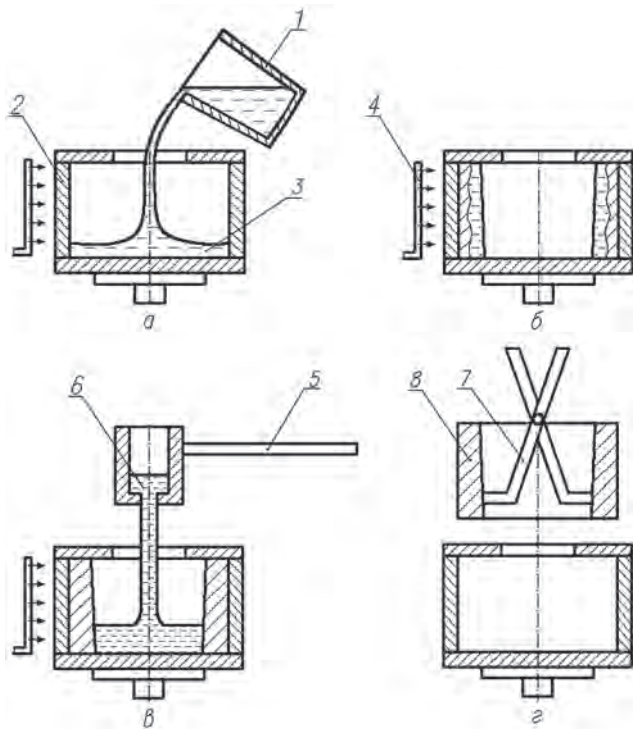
Схема охлаждения отливок из силумина АК15М3 при вертикальном центробежном литье: а – заполнение изложницы расплавом; б – формирование отливки; в – подача охлаждающей жидкости в полость изложницы; г – извлечение отливки; 1 – заливочное устройство; 2 – расплав; 3 – изложница; 4 – водоспрейерное охлаждающее устройство; 5 – заливочный ковшик; 6 – охладитель; 7 – клещи; 8 – отливка
